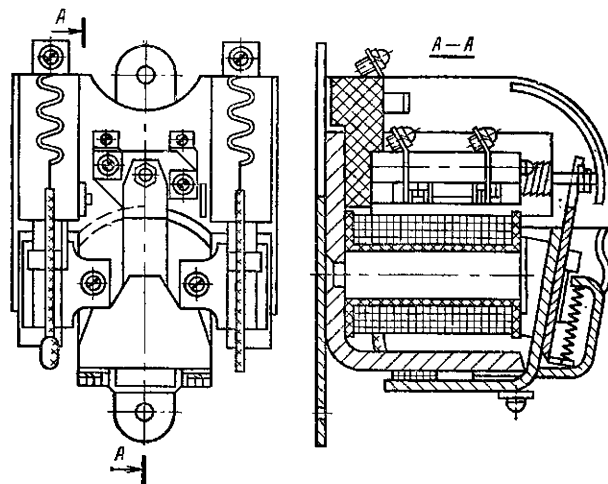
Общий вид контактора типа КПД 121Е.
